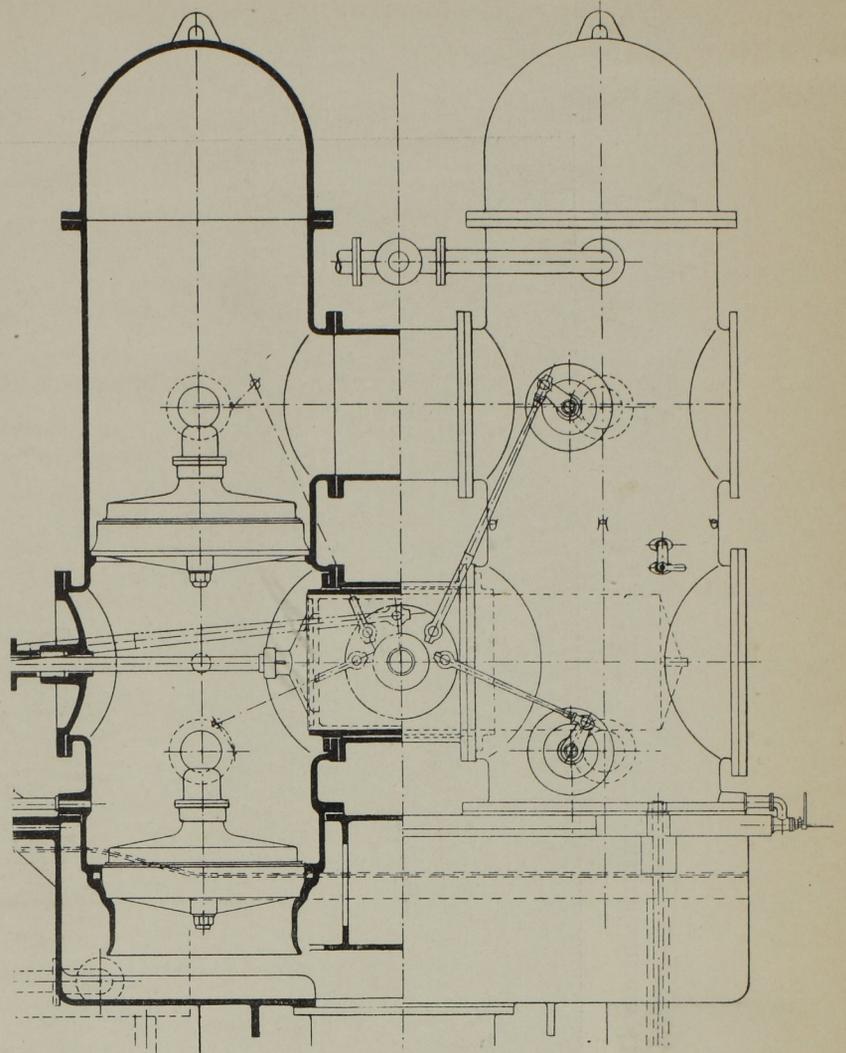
Seitenansicht und Schnitt der Pumpen. Masst. 1:30.
